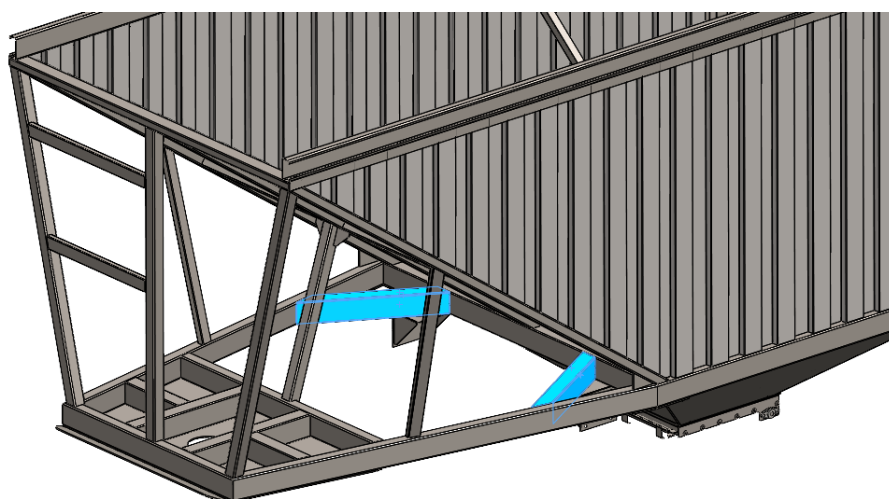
Refuerzos en la estructura para los puntos de apoyo de las patas.
